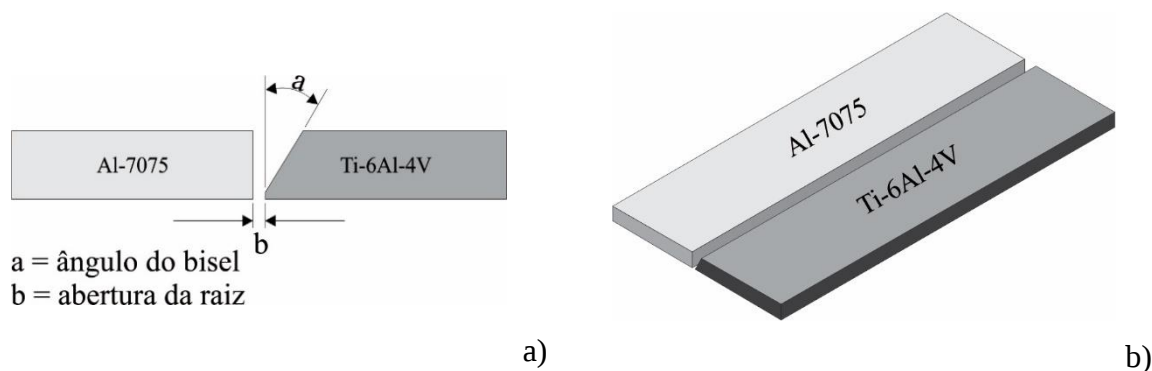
a) Ilustração da seção transversal da junta dissimilar a ser soldada, b) Ilustração em perspectiva da montagem da junta a ser soldada.
